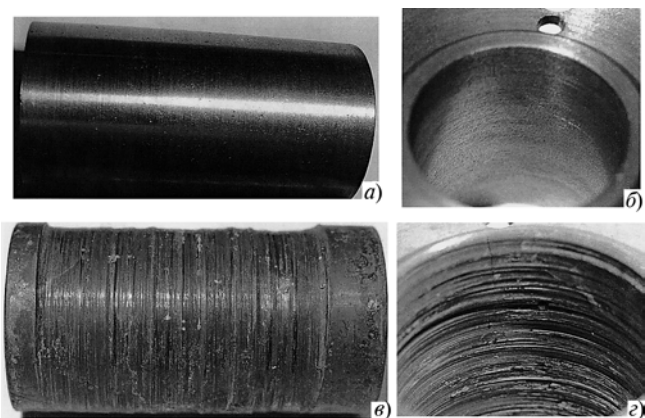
Фотографии втулок вала (а) и подшипника (б) до испытаний и наружной поверхности втулки вала (в) и внутренней поверхности втулки подшипника (г) после 950 ч работы
